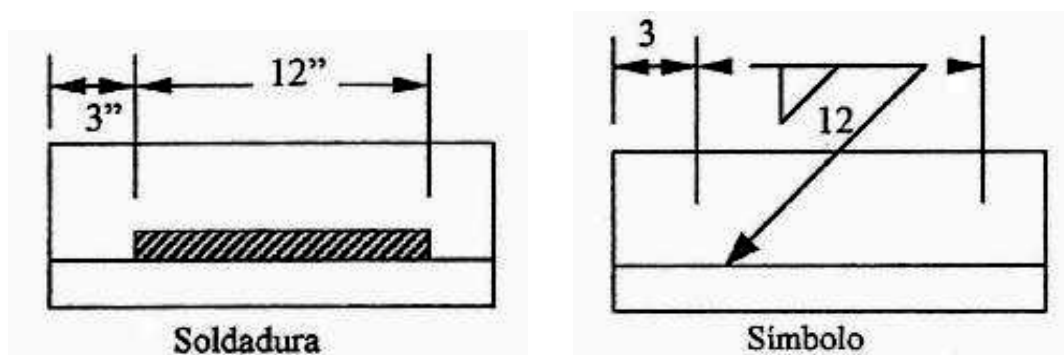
SOLDADURA DE FILETE CON LONGITUD ESPECIFICADA.
